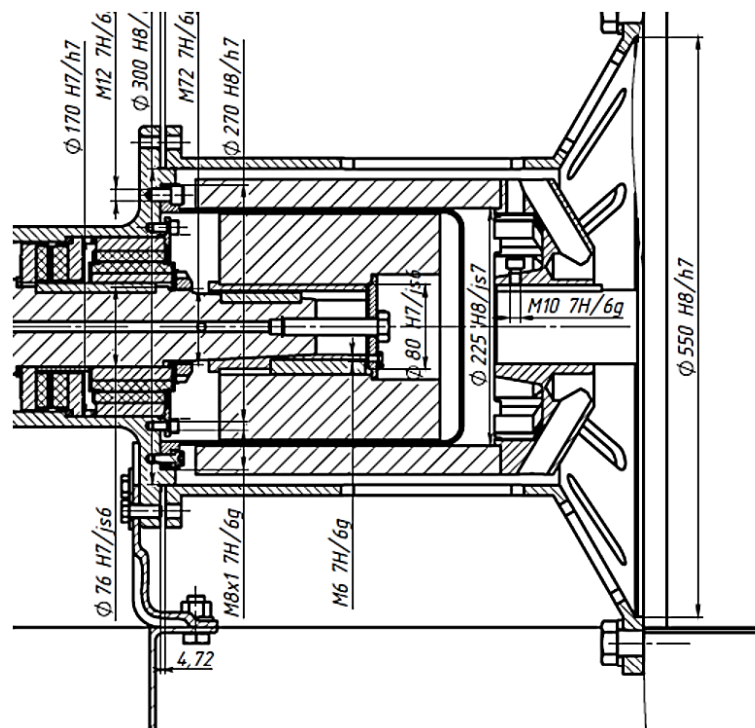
Конструкция внешней магнитной полумуфты и ее защитного кожуха
